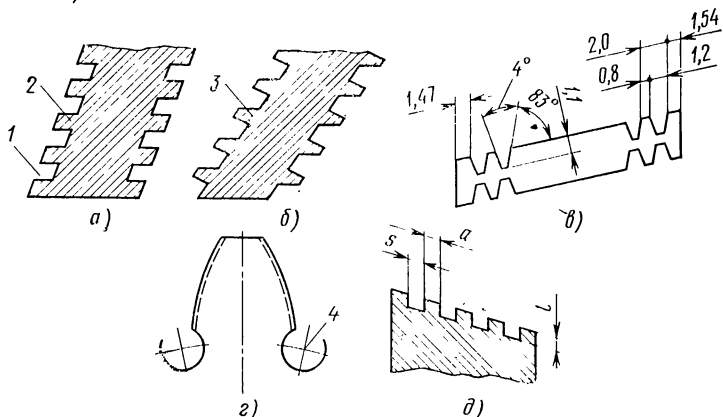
Форма режущих зубчиков шевера и канавок между зубчиками
